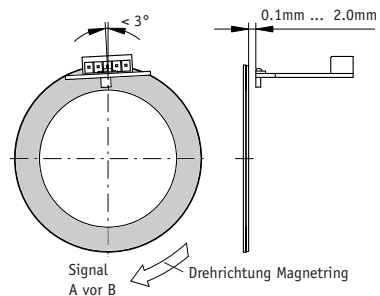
Definition der Zählrichtung mit Magnetring und Montage Sensor/Magnetring, Abstandsmaße, Toleranzen
